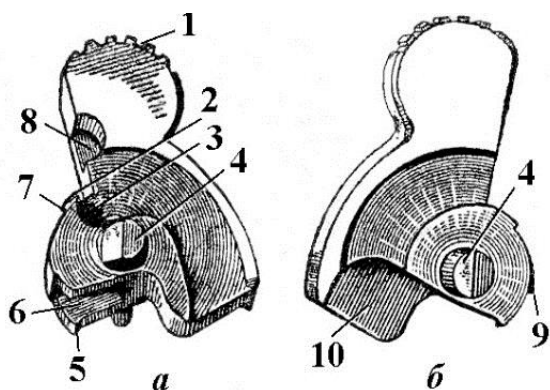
Курок (а — левая сторона; б — правая сторона; 1 — головка с насечкой; 2 — выступ; 3 — выем; 4 — цапфы; 5 — зуб самовзвода; 6 — углубление; 7 — предохранительный взвод; 8 — вырез; 9 — боевой взвод; 10 — кольцевой выем)
